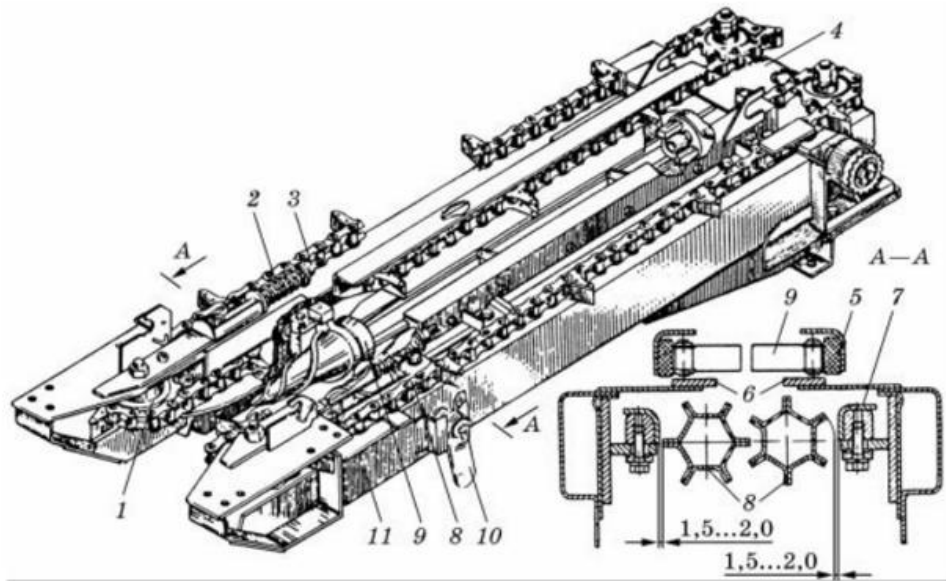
Качанно-відокремлюючий апарат: 1 – натяжна зірочка; 2 – пружина; 3 – натяжний пристрій; 4 – роздавальна коробка; 5 – полозок; 6 – відривні пластини; 7 – чистик; 8 – вальці; 9 – подавальний ланцюг; 10 – важіль для регулювання зазору між вальцями; 11 – рама
